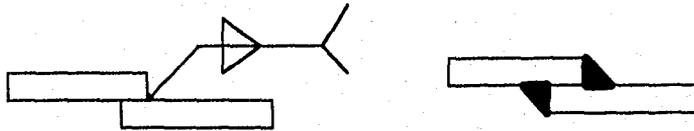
Aplicación de la soldadura por el lado inferior del chaflán.
